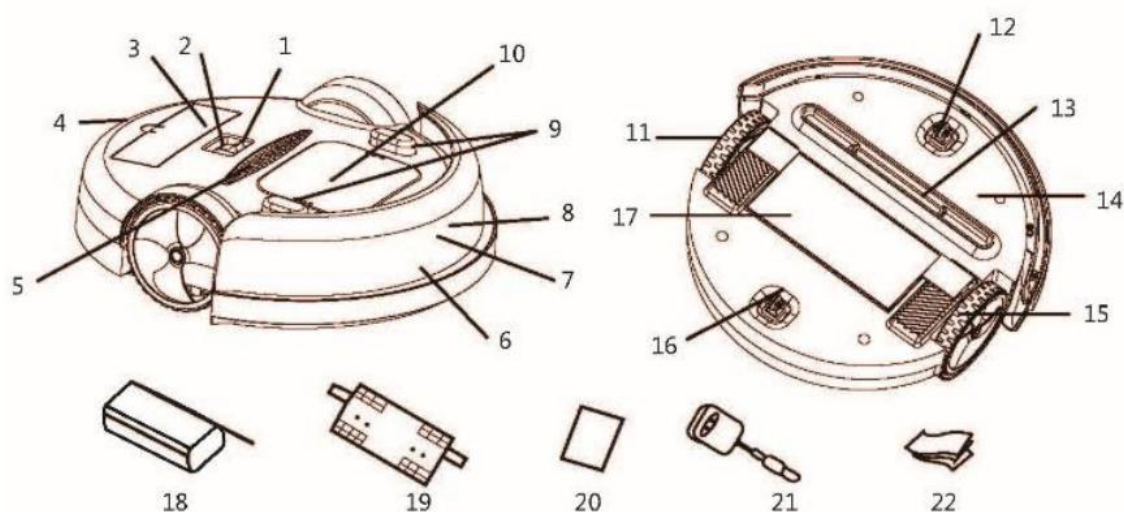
Внешний вид используемого корпуса робота-пылесоса.
